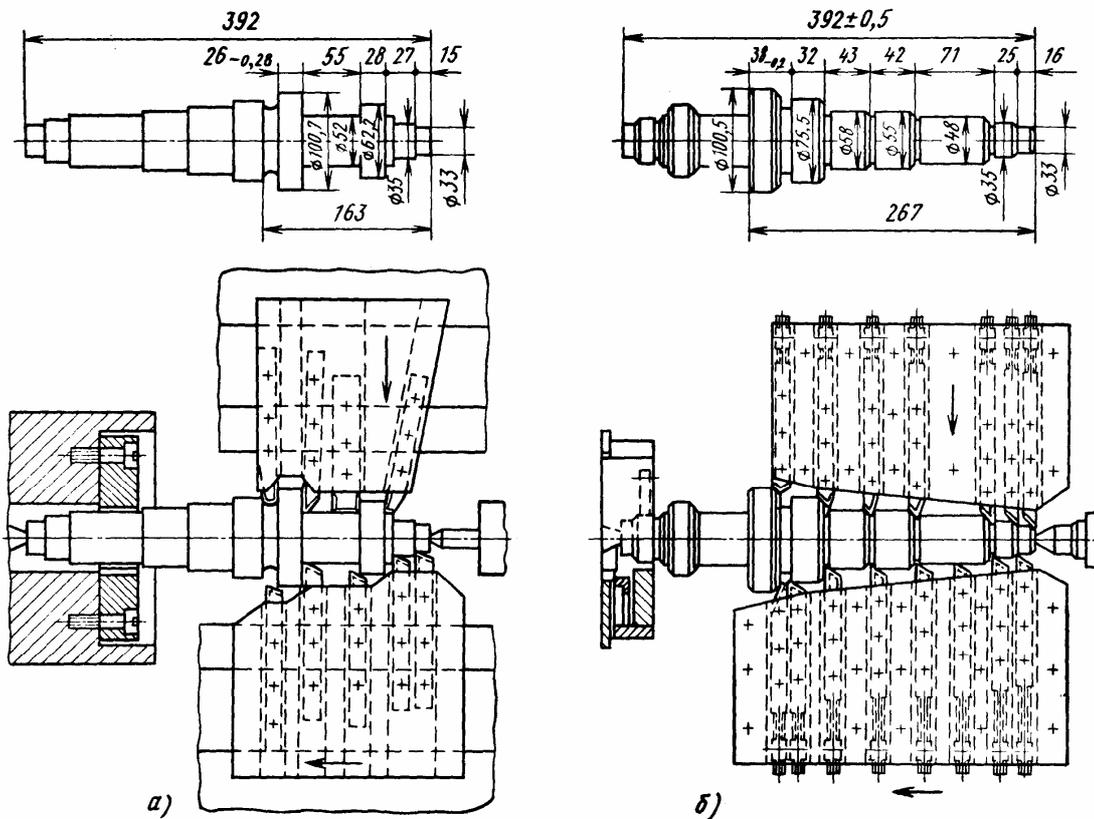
Наладка токарно-многолезцовых полуавтоматов для полной токарной обработки ступенчатого двухстороннего валика:
